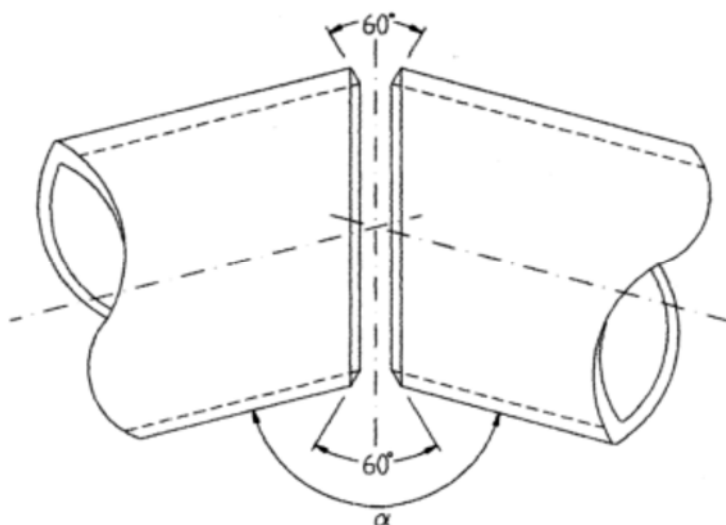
Подготовка и подгонка контуров сварных швов для соединений с разделкой кромок замкнутых профилей.
